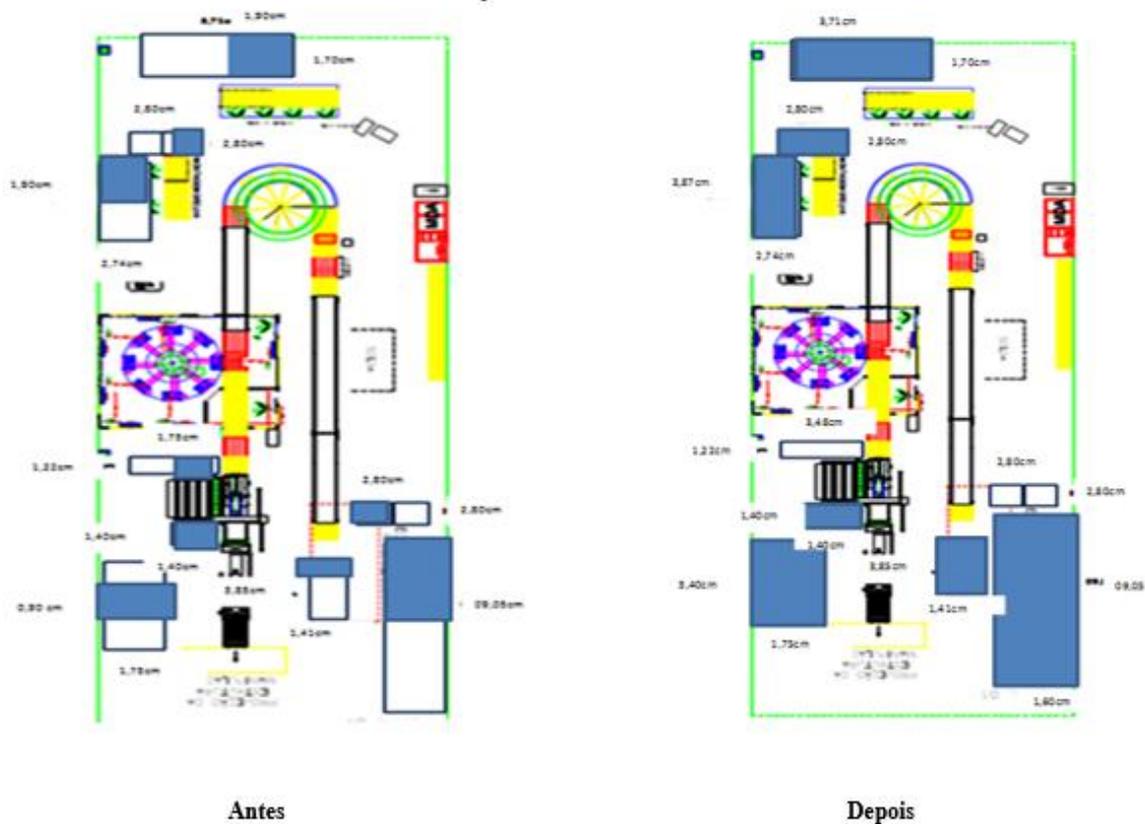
Layout definido da área de abastecimento de materiais de JIT.
